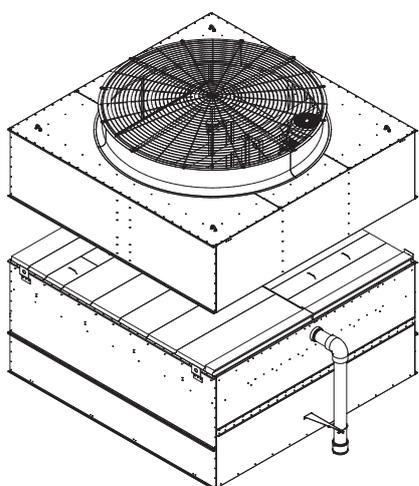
Accoppiamento della sezione ventilatore sulla sezione pacco
